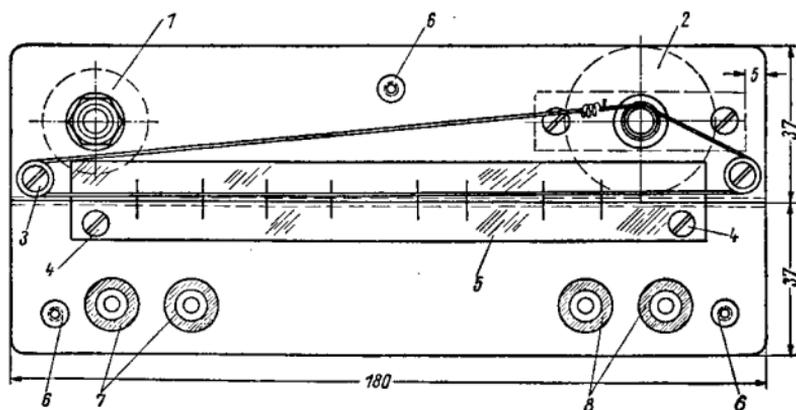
Frontplatte mit Seilführung für die Skala 1 — Potentiometer R 7; 2 — induktive Abstimmung; 3 — Umlenkrollen; 4 — Befestigungsschrauben für die Skala; 5 — Skala; 6 — 3 Abstandsstücke, 6 mm Dmr., 15 mm lang mit Gewinde M 3 zur Deckelbefestigung; 7 — Buchsen für Hörer; 8 — Buchsen für Peilrahmen
